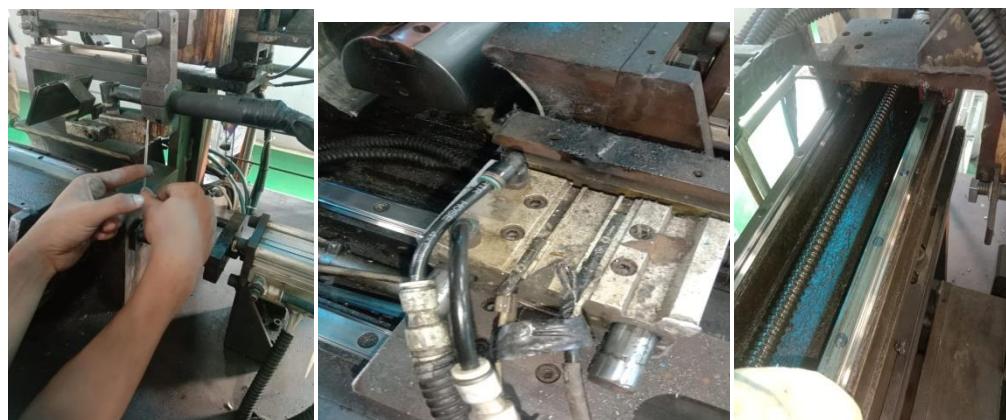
Dokumentasi Inspeksi Mesin Welding
